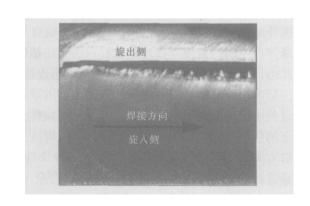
焊缝表面的沟槽缺陷 Fig 2 Groove in well surface
